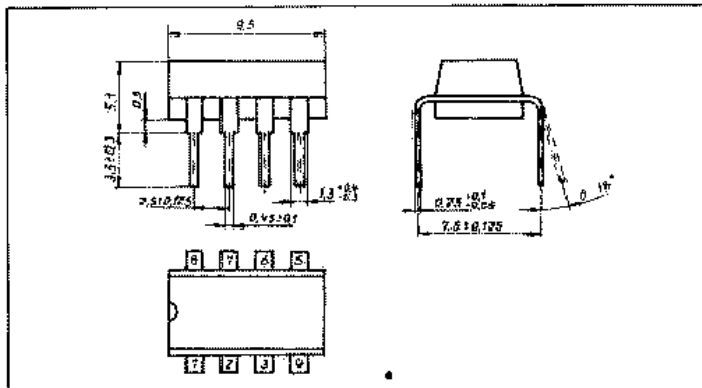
Abmessungen der Typen B 060, B 061, B 062, B 066
